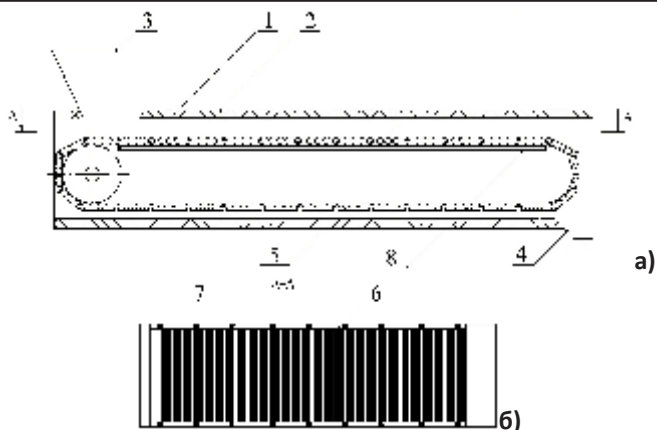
Конструкция предложенной жомосушилки непрерывного типа
